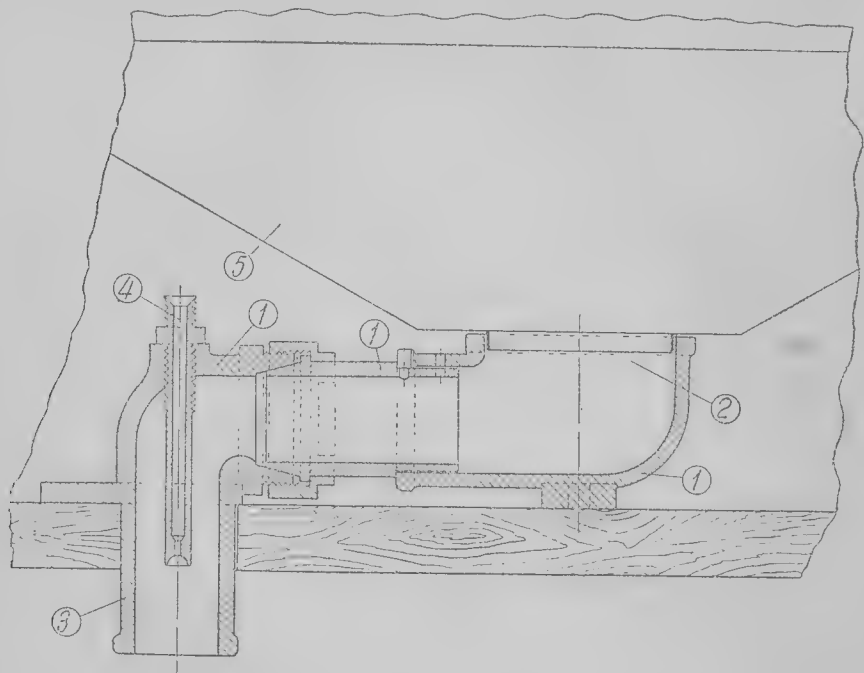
Воздушная песочница Плащинского: 1 — корпус, 2 — отверстие, 3 — патрубок, 4 — сопло, 5 — песочный ящик.
